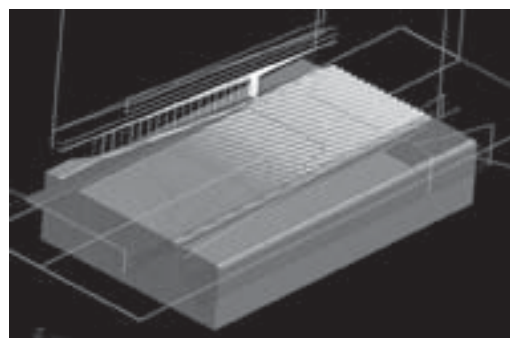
Трёхмерная модель резьбонакатной плашки, импортированная из КОМПАС-3D в GeMMA-3D и траектории перемещений режущего инструмента
